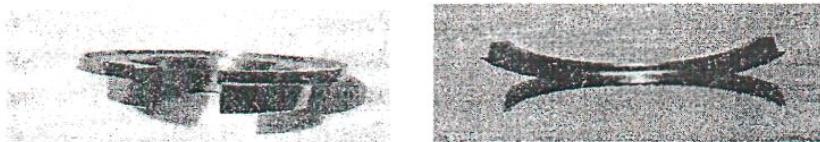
Заготовки з зовнішнім і внутрішнім буртом, отримані висадкою з цілеспрямованим зміщенням вершини конічного валка
